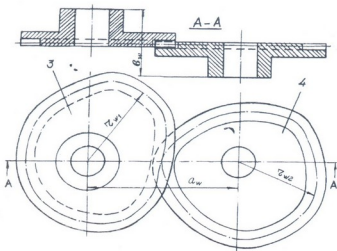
Торцовая зубчатая передача с некругло-круглыми зубчатыми колесами
